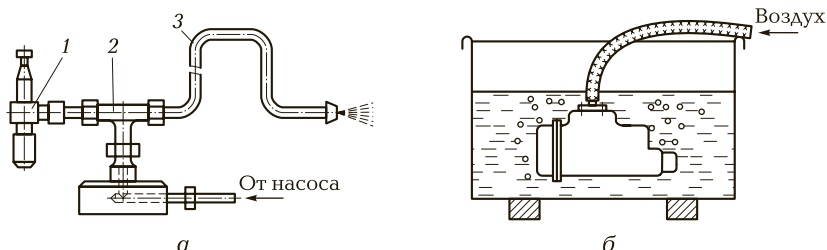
Приспособление для гидравлических испытаний трубопроводов (а) и испытание сборочных единиц на герметичность сжатым воздухом (б):
